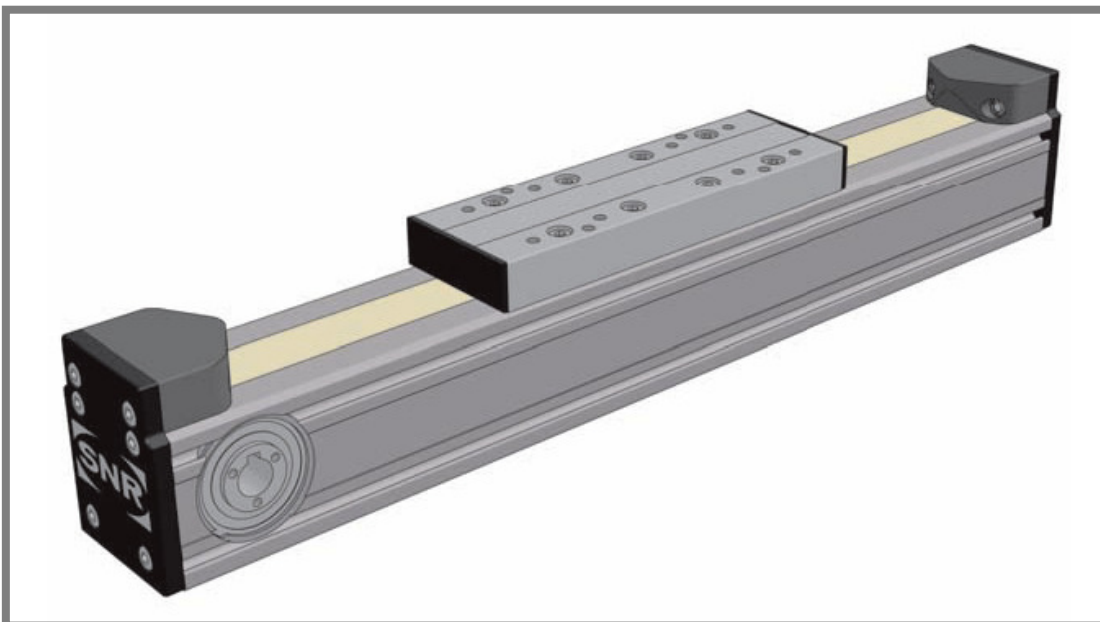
Detail ručně poháněného odměřovacího systému se zakrytovanou magnetickou páskou
